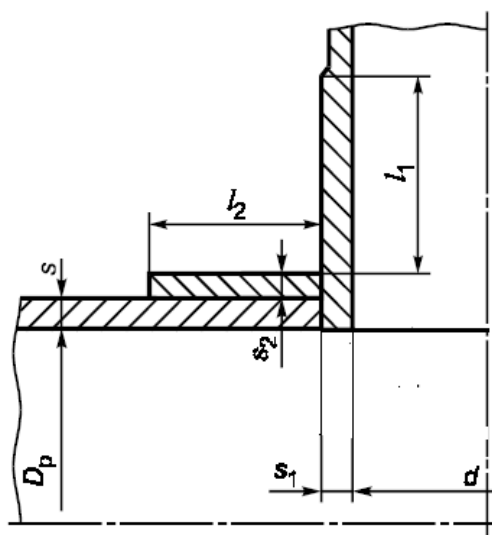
Укрепление отверстий при наличии проходного штуцера
